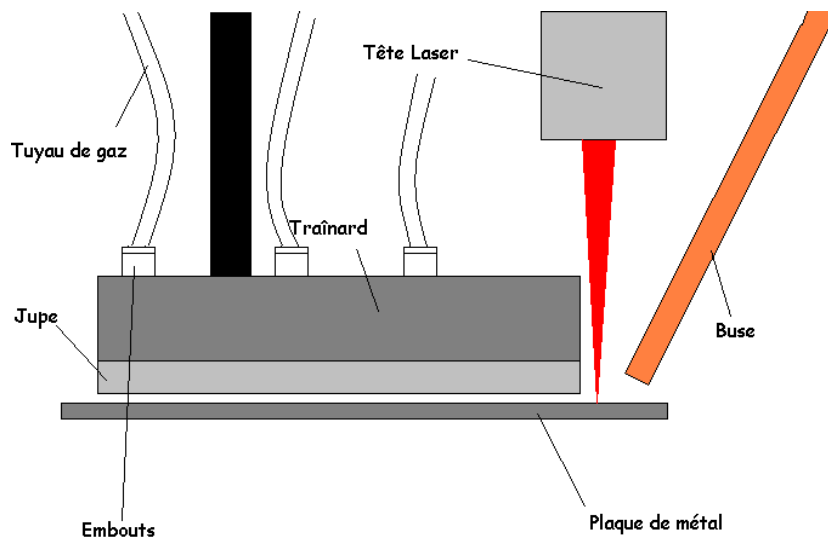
La configuration de soudage pour l'assemblage TA6V-cuivre-inox par laser.
